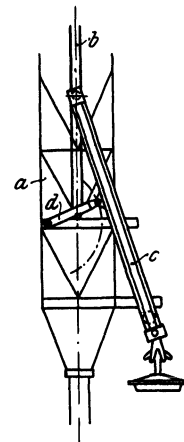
Tiefendeckel-Abhebevorrichtung (Neunkirchen).
